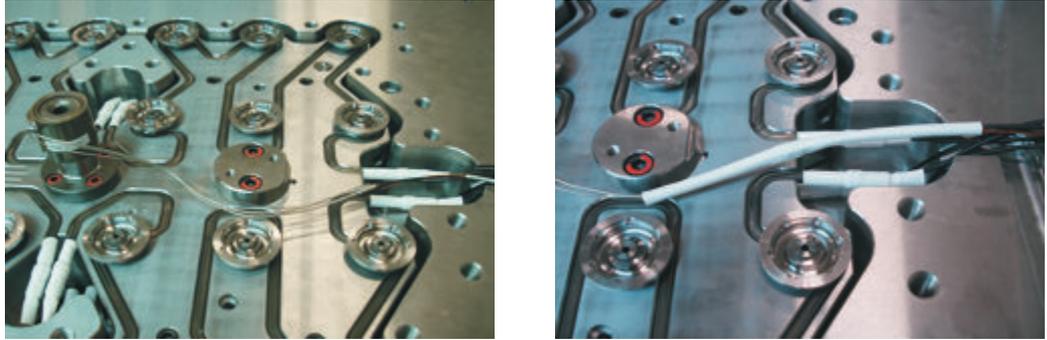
Kabelschlauch aus Glasfaser (Beispiel)
